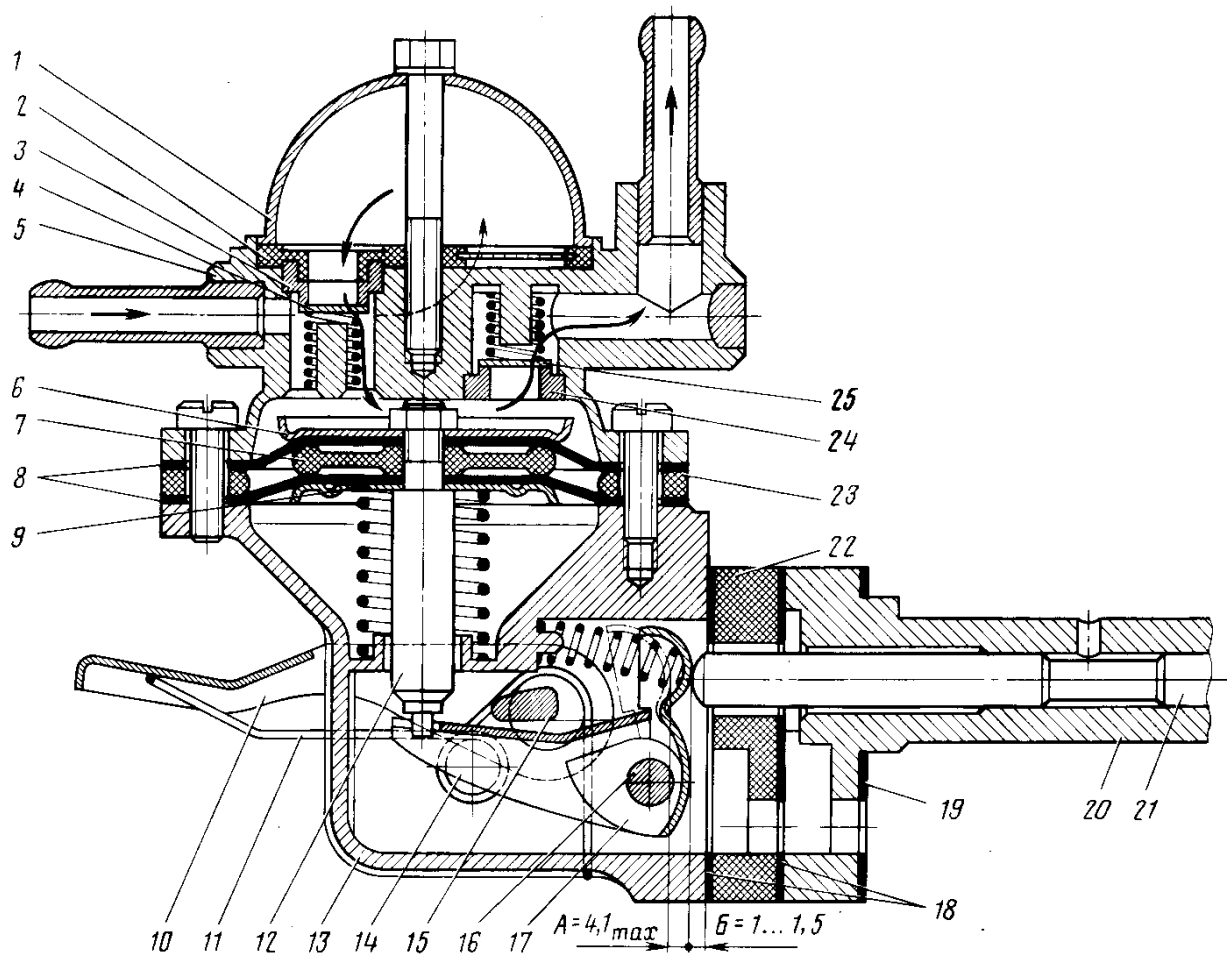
Топливный насос: 1 — крышка; 2 — фильтр; 3 — пробка седла впускного клапана; 4 — впускной клапан; 5 — верхняя часть корпуса; 6 — верхняя чашечка диафрагмы; 7 — внутренняя дистанционная прокладка; 8 — диафрагма; 9 — нижняя чашечка диафрагмы; 10 — рычаг; 11 — пружина рычага; 12 — шток; 13 — нижняя часть корпуса; 14 — баланси́р; 15 — эксцентрик; 16 — ось рычага и баланси́ра; 17 — рычаг привода; 18 — прокладки; 19 — регулировочная прокладка; 20 — направляющая штанги привода насоса; 21 — штанга; 22 — проставка; 23 — дистанционная прокладка; 24 — пробки седла нагнетающего клапана; 25 — нагнетающий клапан; А — конец рабочего хода; Б — начало рабочего хода
